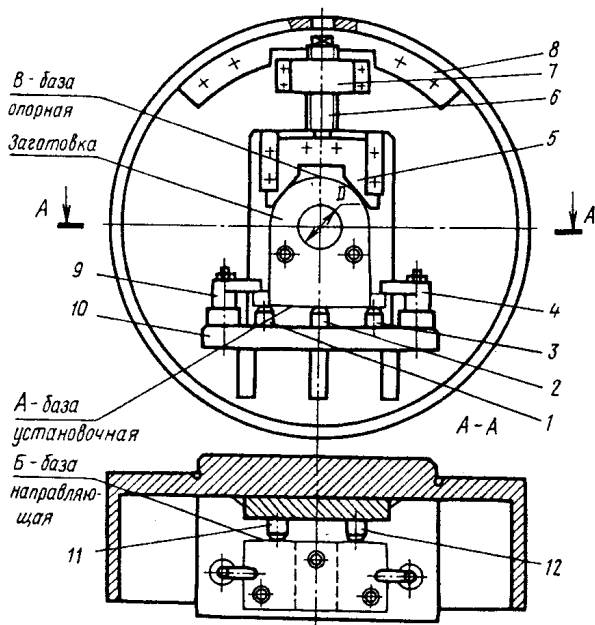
Конструкция токарного приспособления для растачивания отверстия в корпусе:
